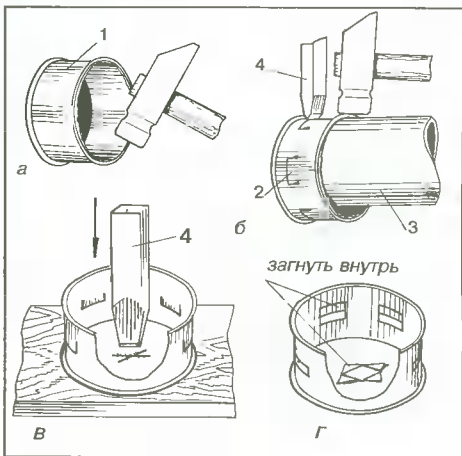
Изготовление установочной коробки из консервной банки: а — подгиб во внутрь острого края банки; б — окончательный догиб кромок и пробивание установочных отверстий на боковых стенках; в — пробивание отверстия в дне; г — оформление контура отверстия. 1 — консервная банка; 2 — П-образная щель; 3 — массивная труба; 4 — зубило; 5 — молоток.
